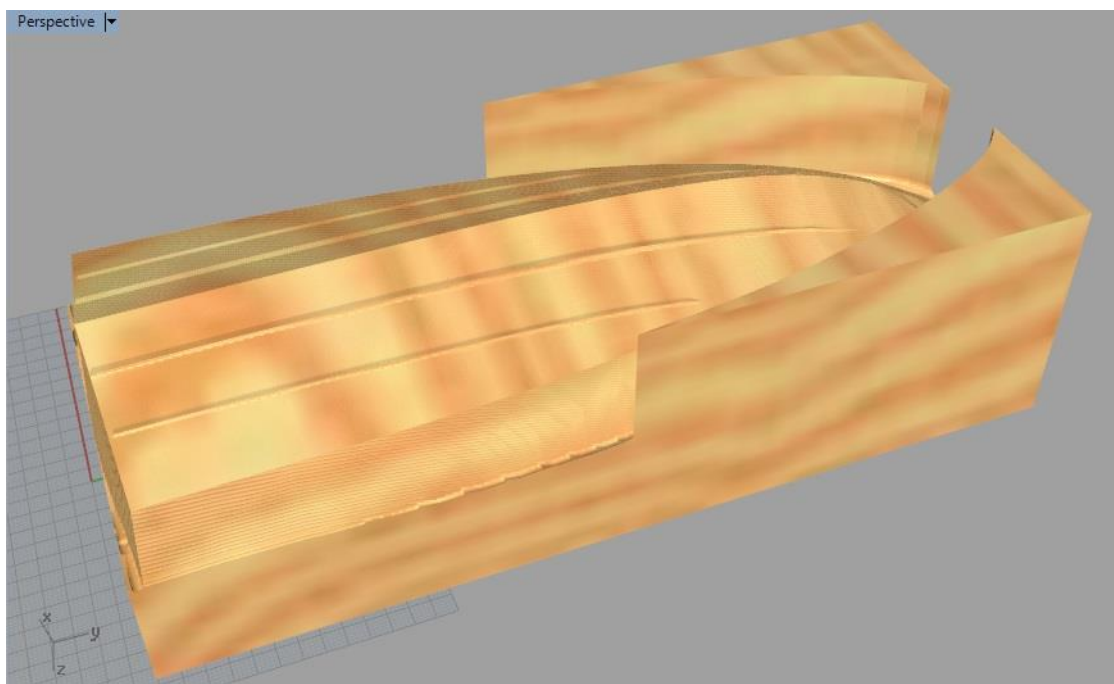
Анимированный вариант фрезеровки нижней части корпуса 3D-модели гоночной лодки
